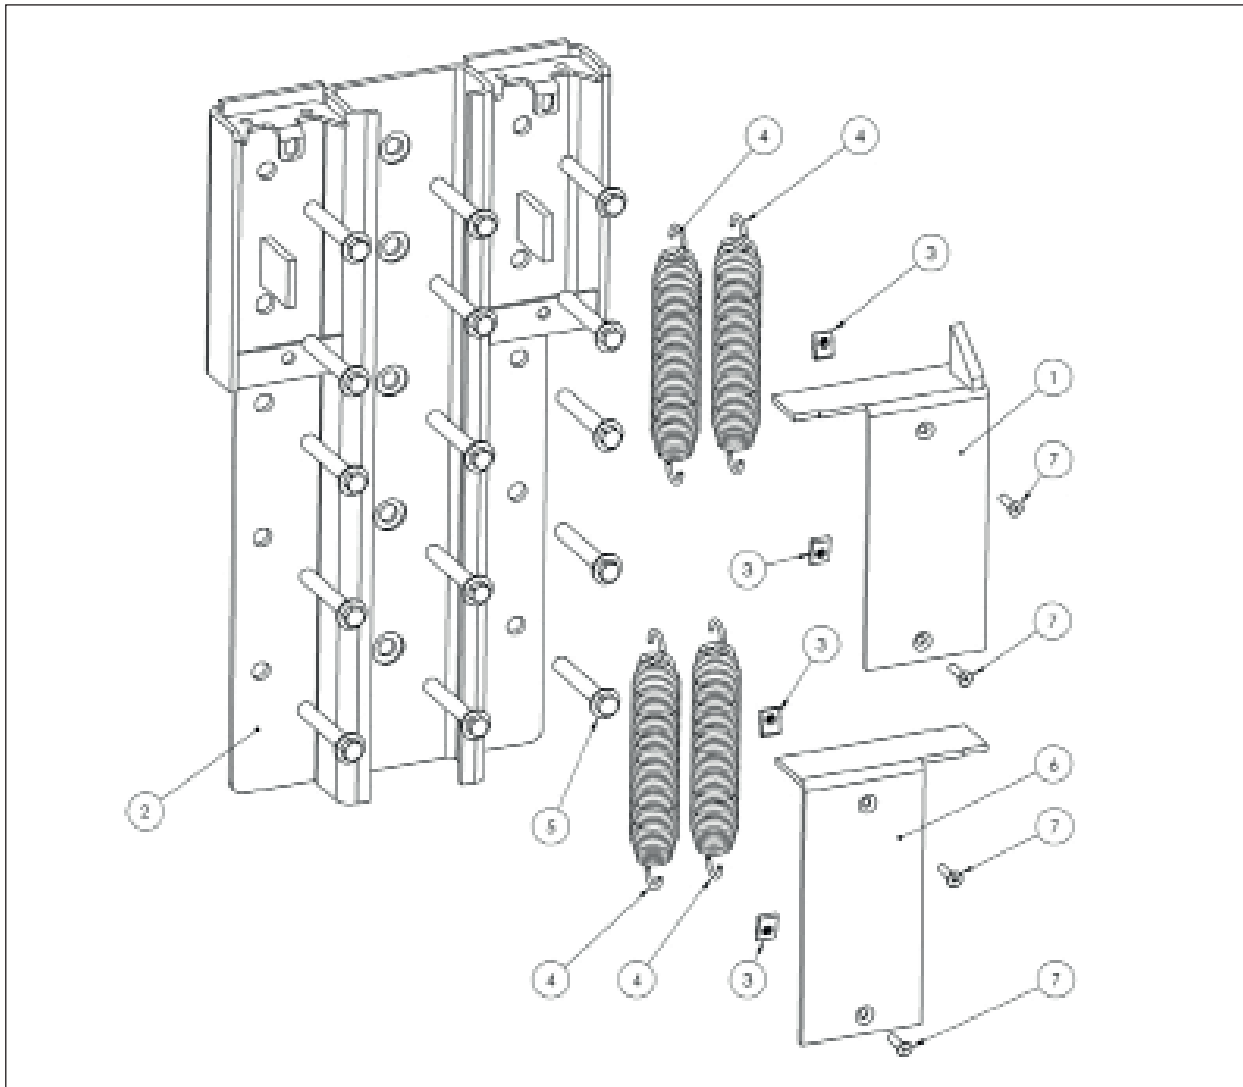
FIGURA AN—CONJUNTO DE GUÍA DE RODILLOS
